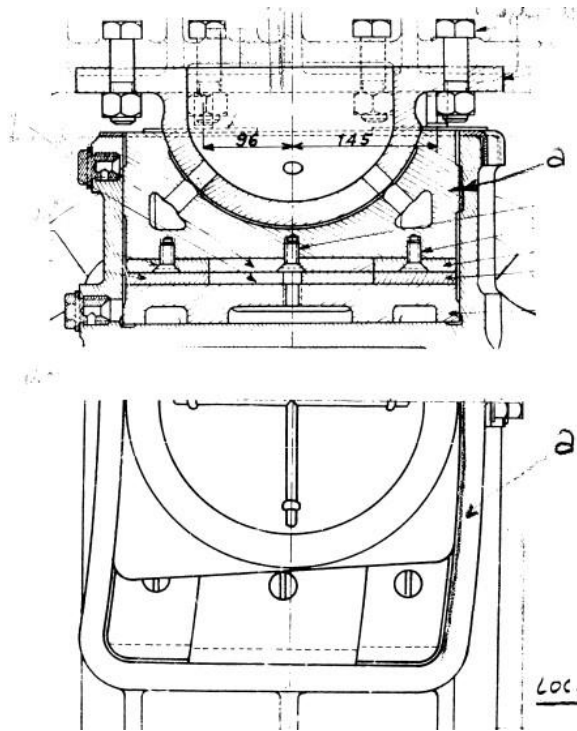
Pivot et crapaudine - Plan Schneider - Archives SNCF, Le Mans.
